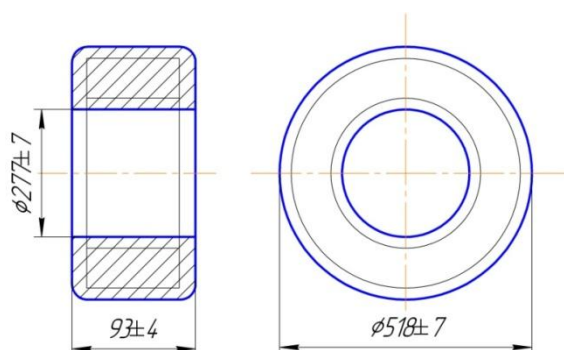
Поковка кольца с припусками и допусками
